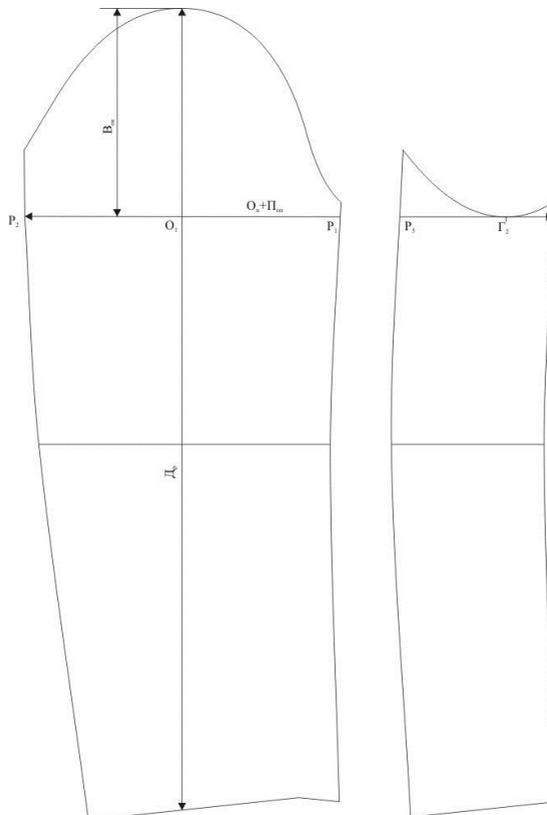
Проверка основных размеров чертежа рукава
